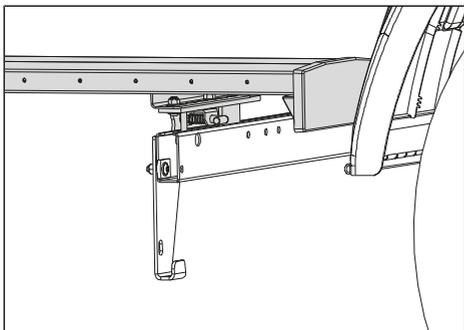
Dispositivo di protezione laterale orientabile sollevato
